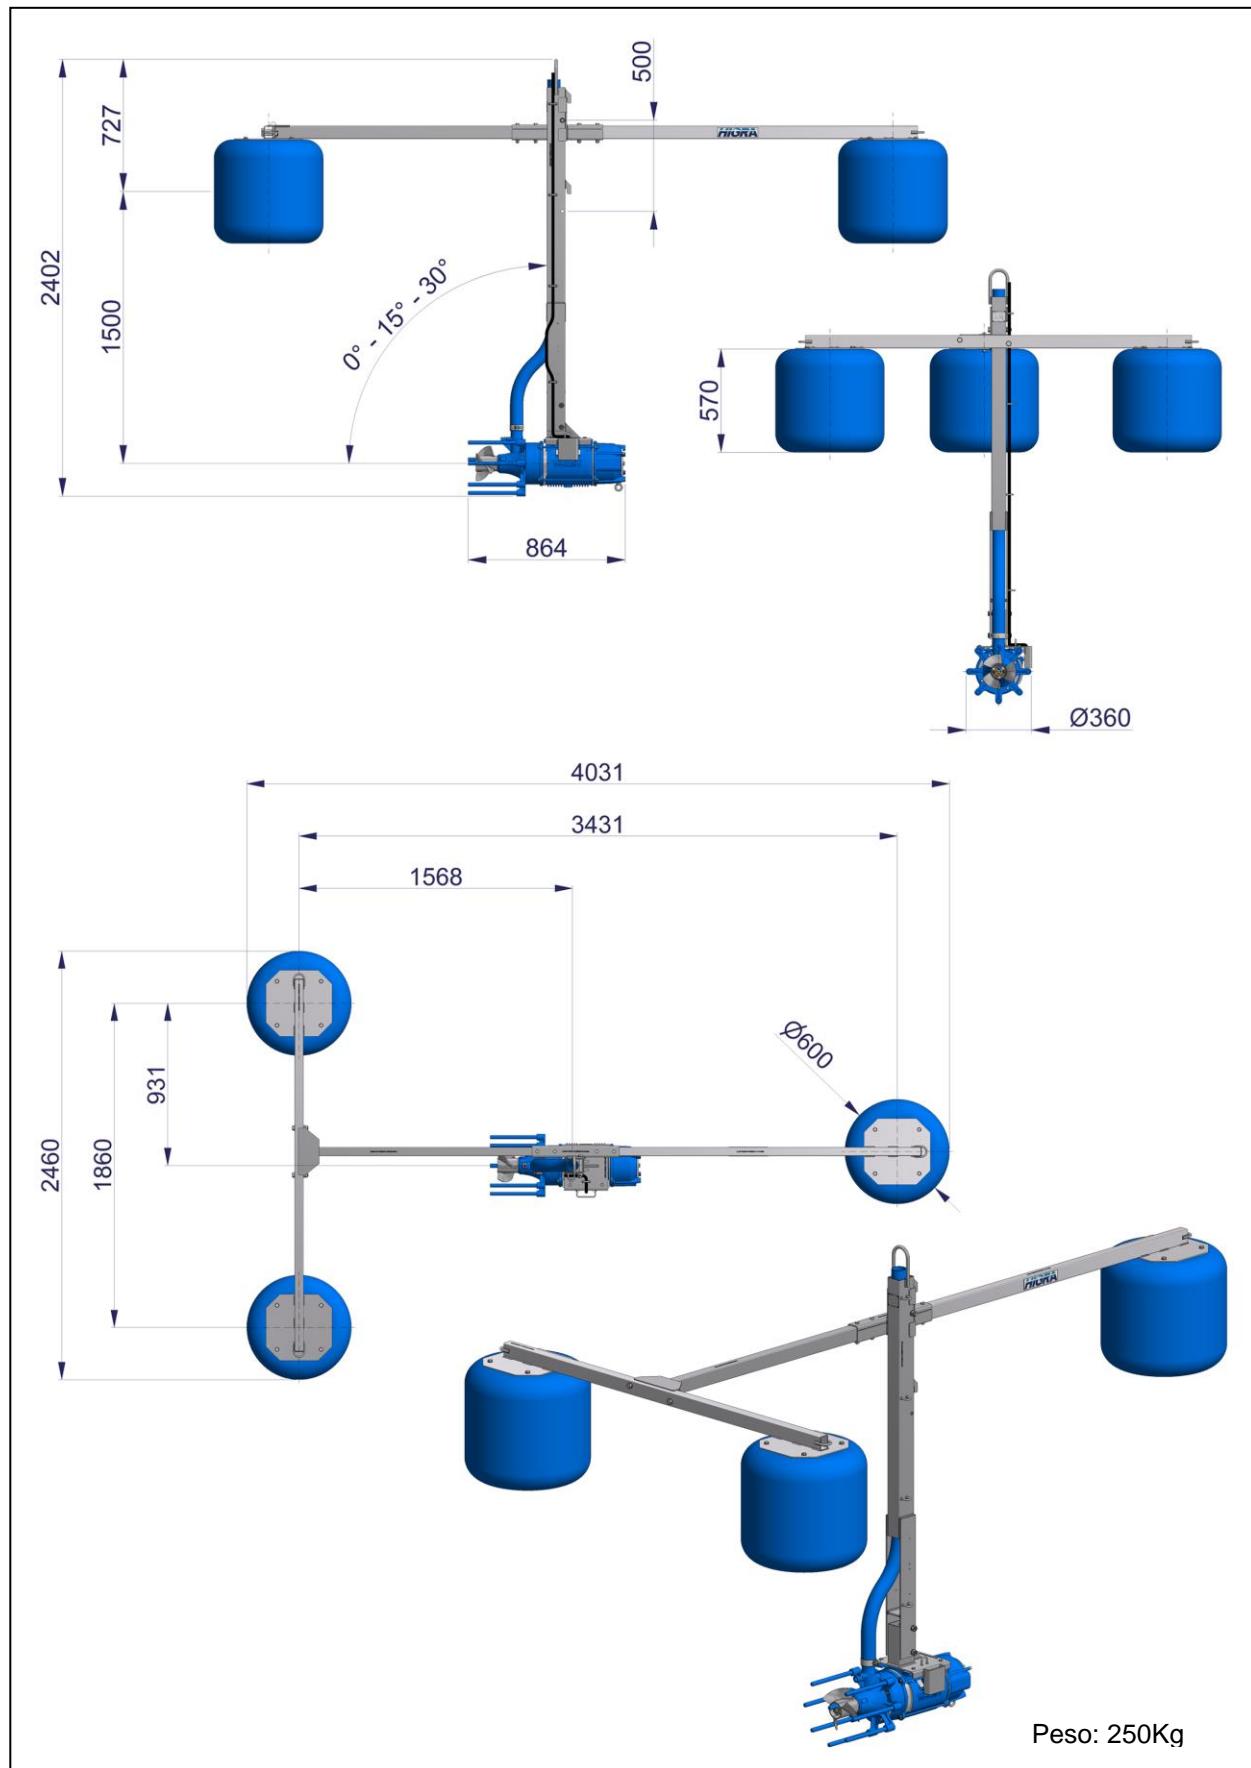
Dimensional TORNADO 10, 12,5, 15 e 20CV
